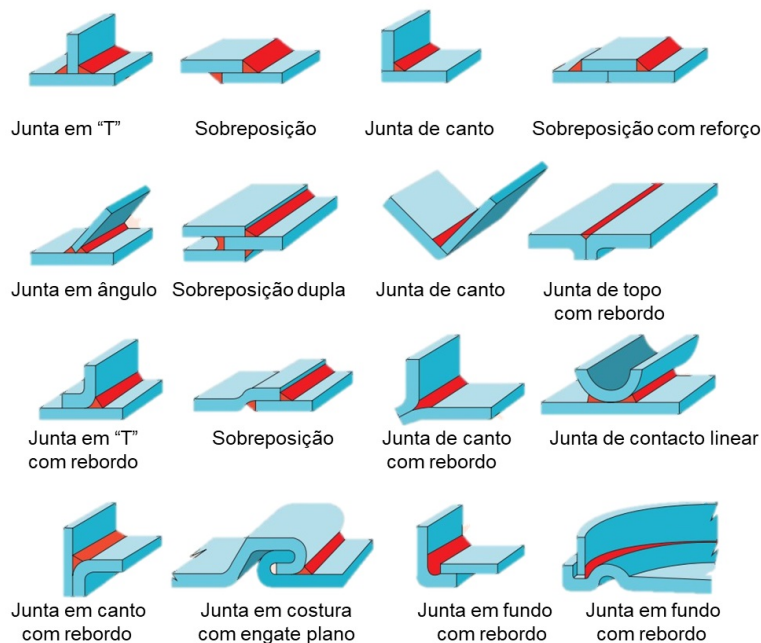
Configurações típicas de juntas soldadas por transmissão. Adaptado de [15].
